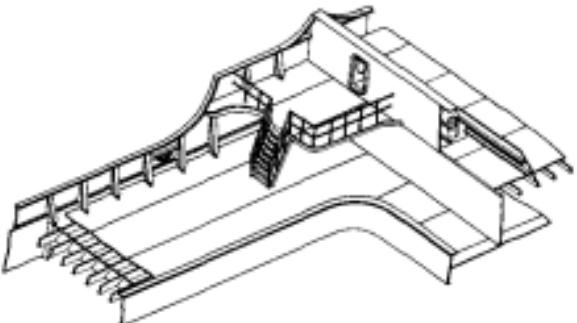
Высотный бак и длинная переходная кианца от надстройки короткого бака к фальшборту
